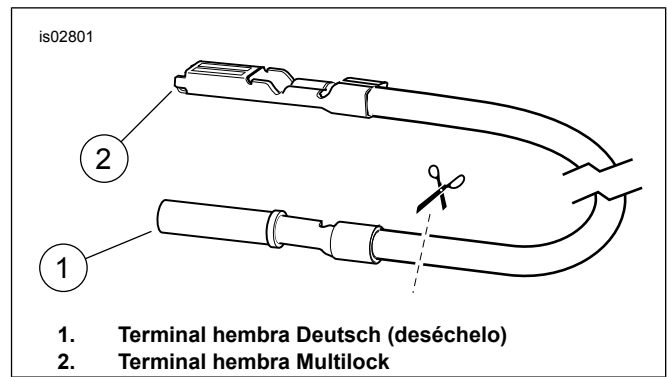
Corte del terminal Deutsch del cable conductor del adaptador
